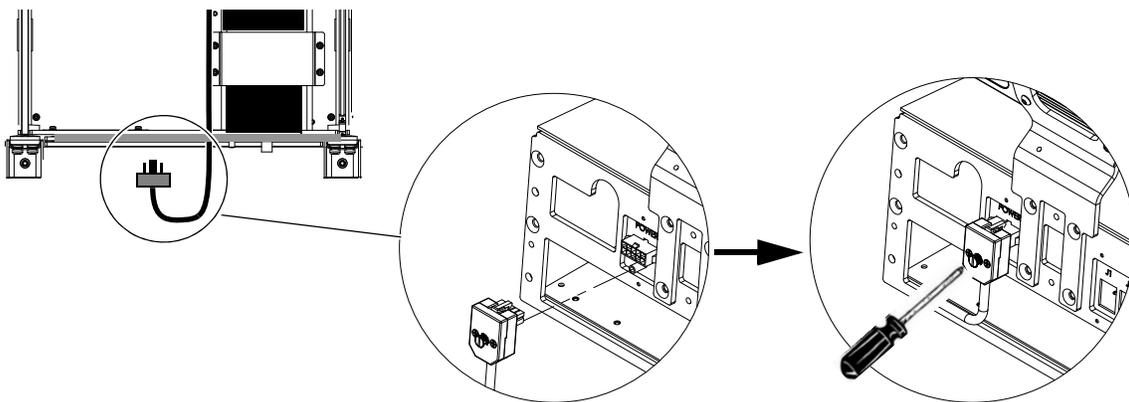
Conexión del terminal del cable a la placa de unión posterior
